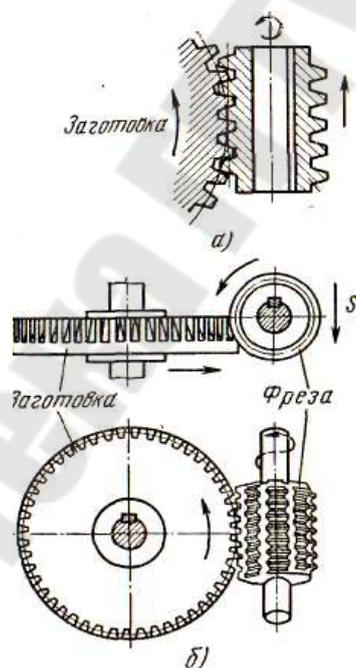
Схема нарезания зубьев червячной фрезой
